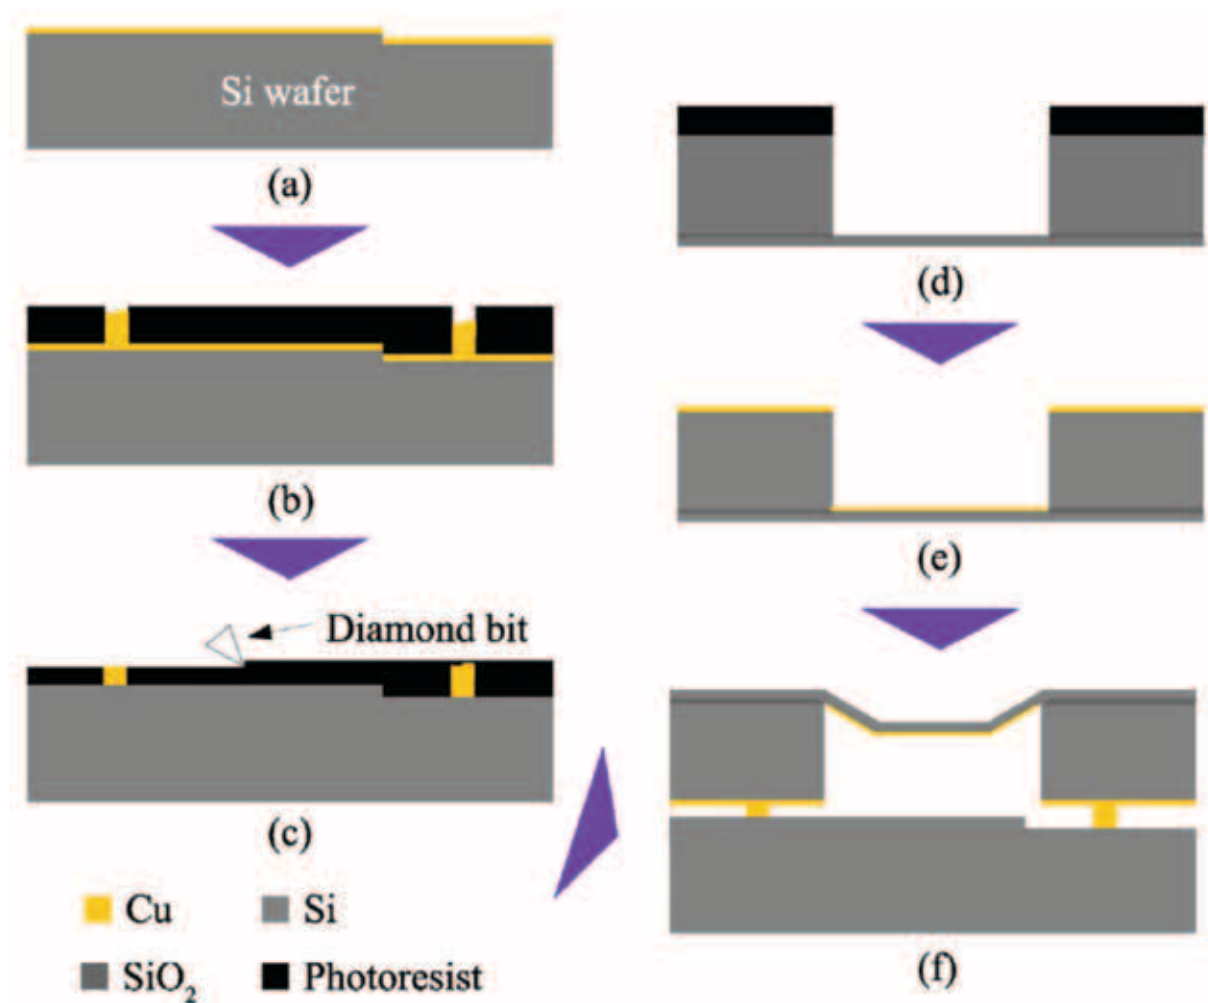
Процесс изготовления испытательного устройства для склеивания.
